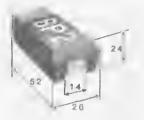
Внешний вид и размеры корпуса DO-214AC
